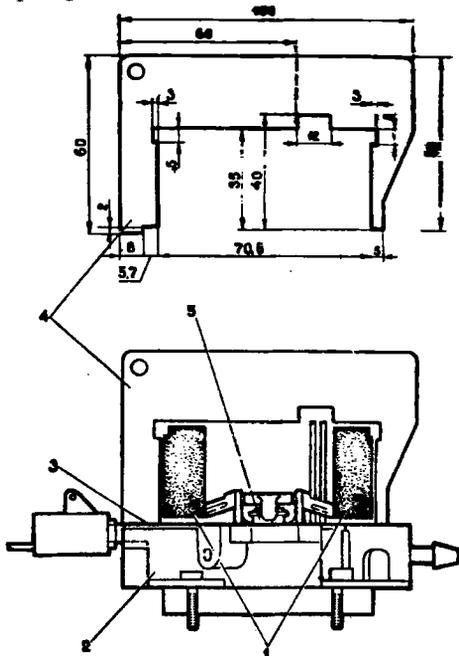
Установка уровня топлива в поплавковой камере карбюратора 21053-1107010: 1 - поплавок; 2 - крышка карбюратора; 3 - прокладка; 4 - калибр; 5 - игольчатый клапан
